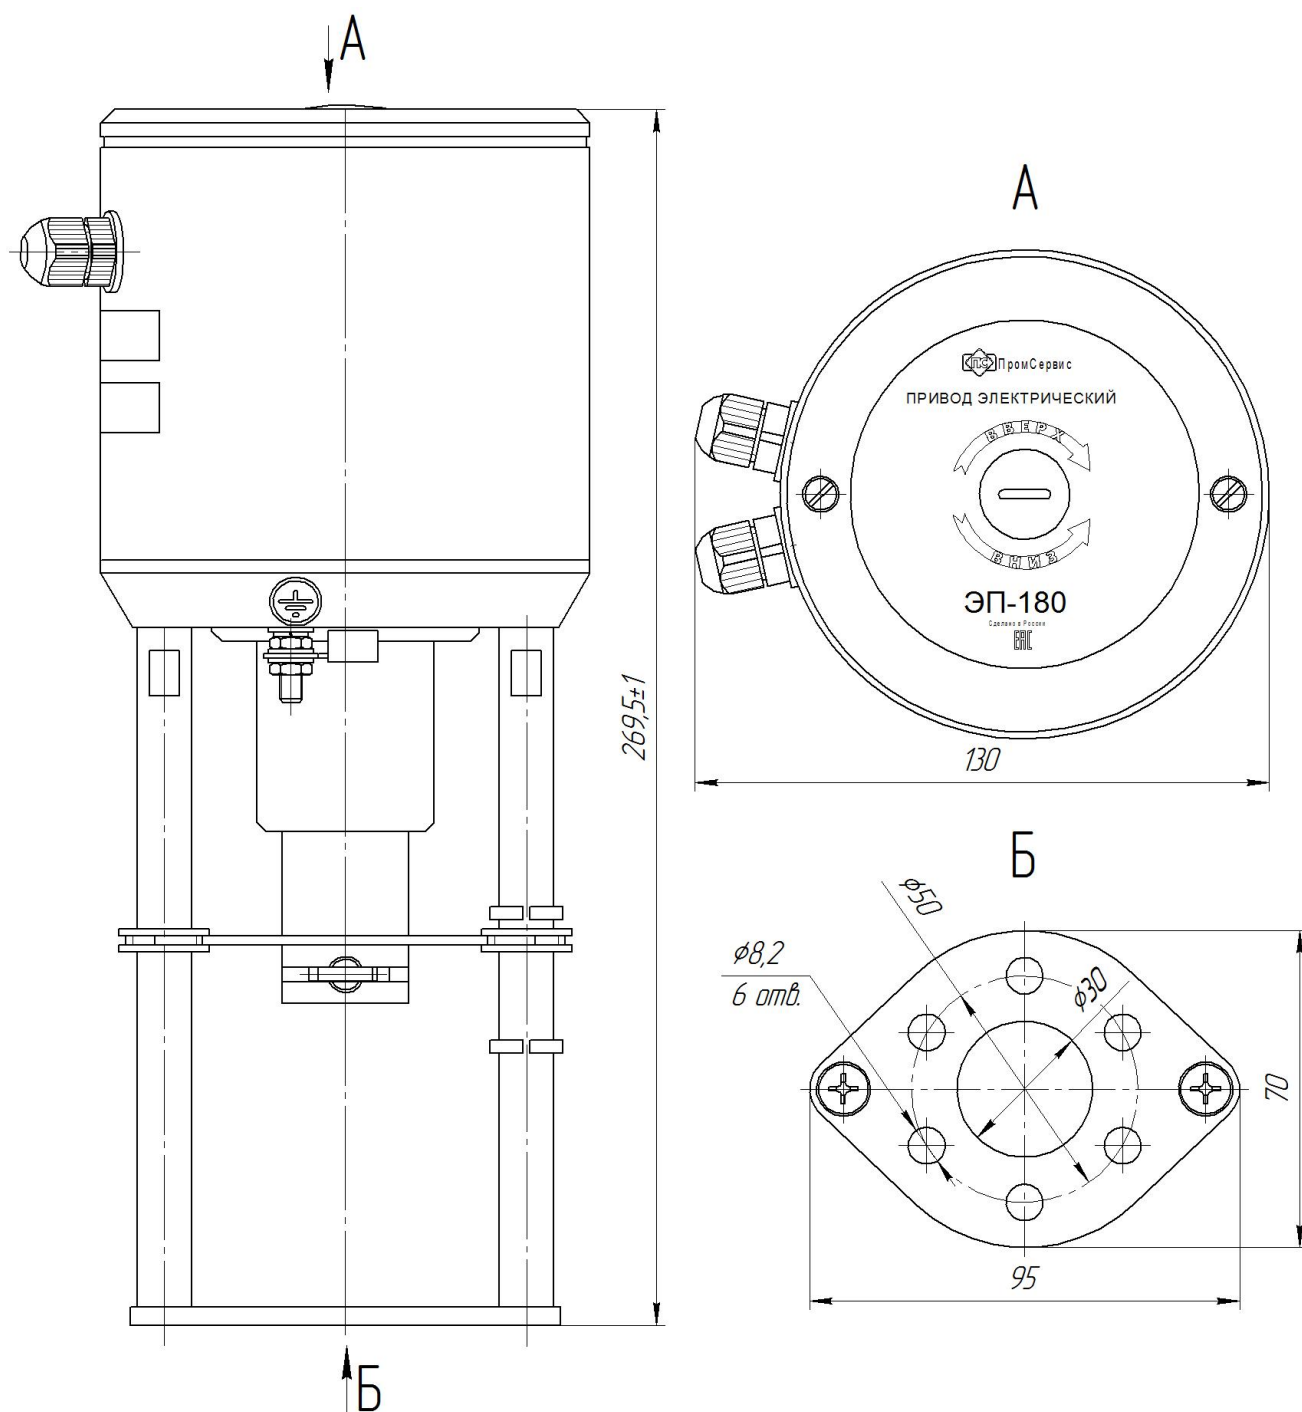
габаритные и присоединительные размеры привода исполнения ЭП-180-02
